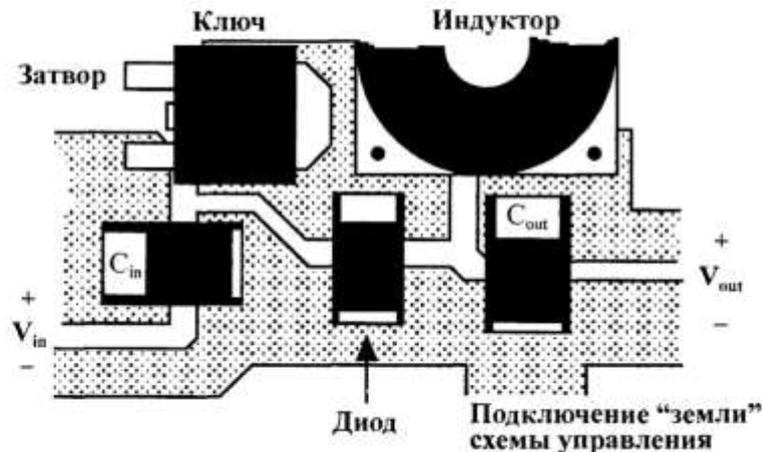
Хорошая компоновка понижающего преобразователя
